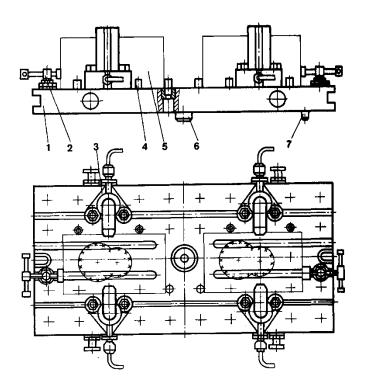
Приспособление двухместное для установки крышки: 1- плита; 2- прижим универсальный; 3- прихват $\Gamma-$ образный; 4- палец цилиндрический; 5- заготовка; 6, 7- пальцы установочные
